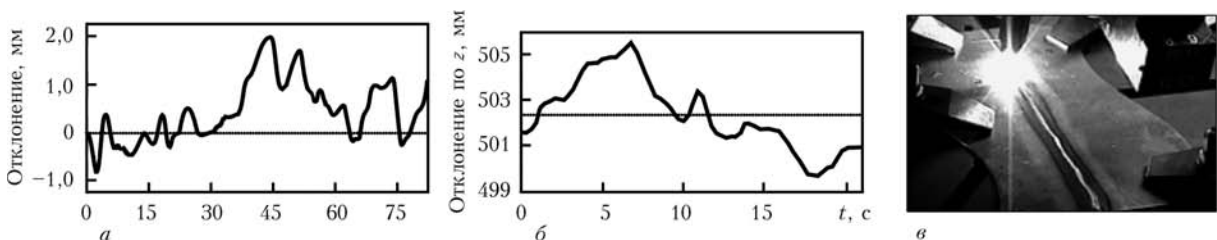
Телеробототехнический процесс сварки прямолинейного шва: а — поперечное отклонение; б — по высоте z; в — процесс сварки
